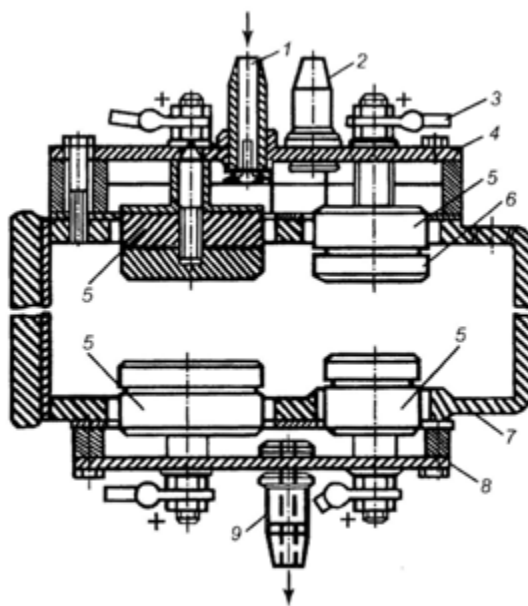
Схема пристрою для проточного залізнення отворів в корпусних деталях: 1 – підвідний штуцер; 2 – штуцер для відведення газів; 3- струмопровід; 4 – верхня кришка; 5 – анод; 6 – гайка; 7 – деталь; 8 – нижня кришка; 9 – зливний штуцер
